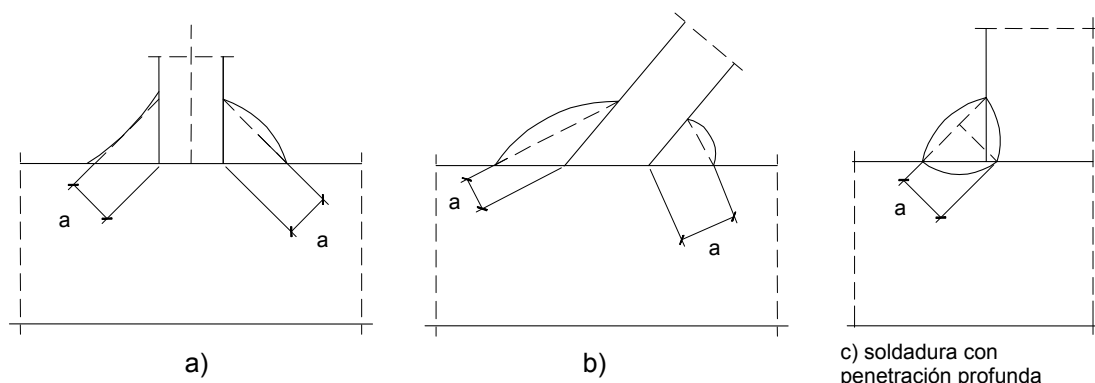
Soldadura en ángulo. Espesor de garganta
